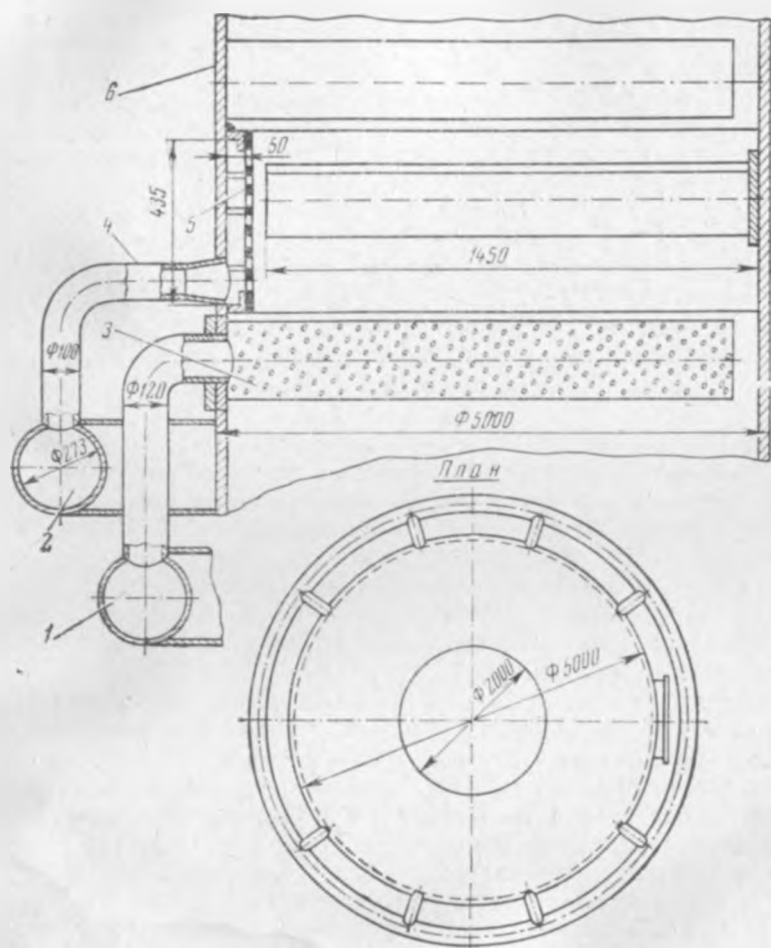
Устройство для дополнительного отбора сока из диффузора КДА-30-66.
